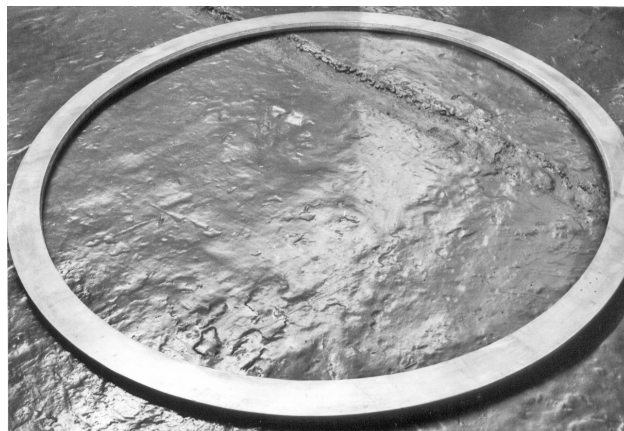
Биметаллическое кольцо сталь – алюминиевый сплав под переходный элемент для соединения двигателя с топливным баком РКТ
